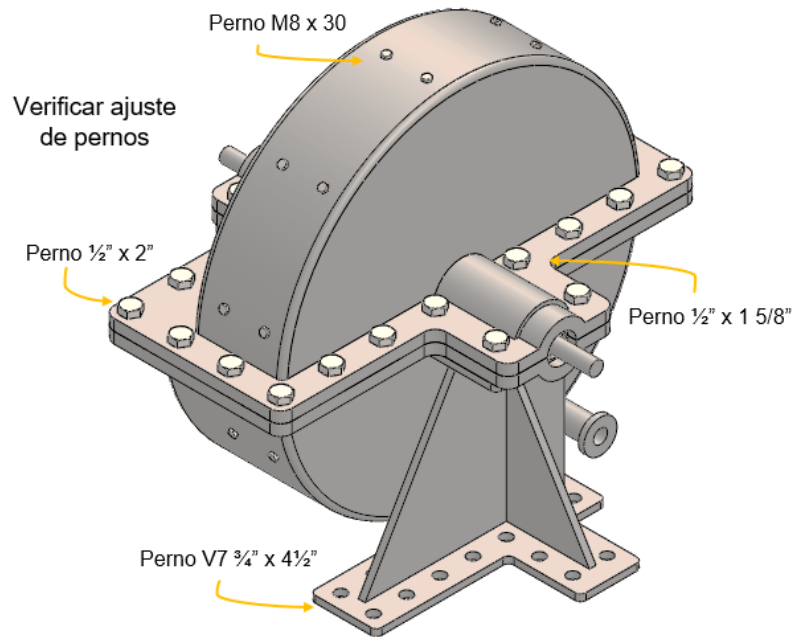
Componentes turbina a gas refrigerante sobrecalentado
